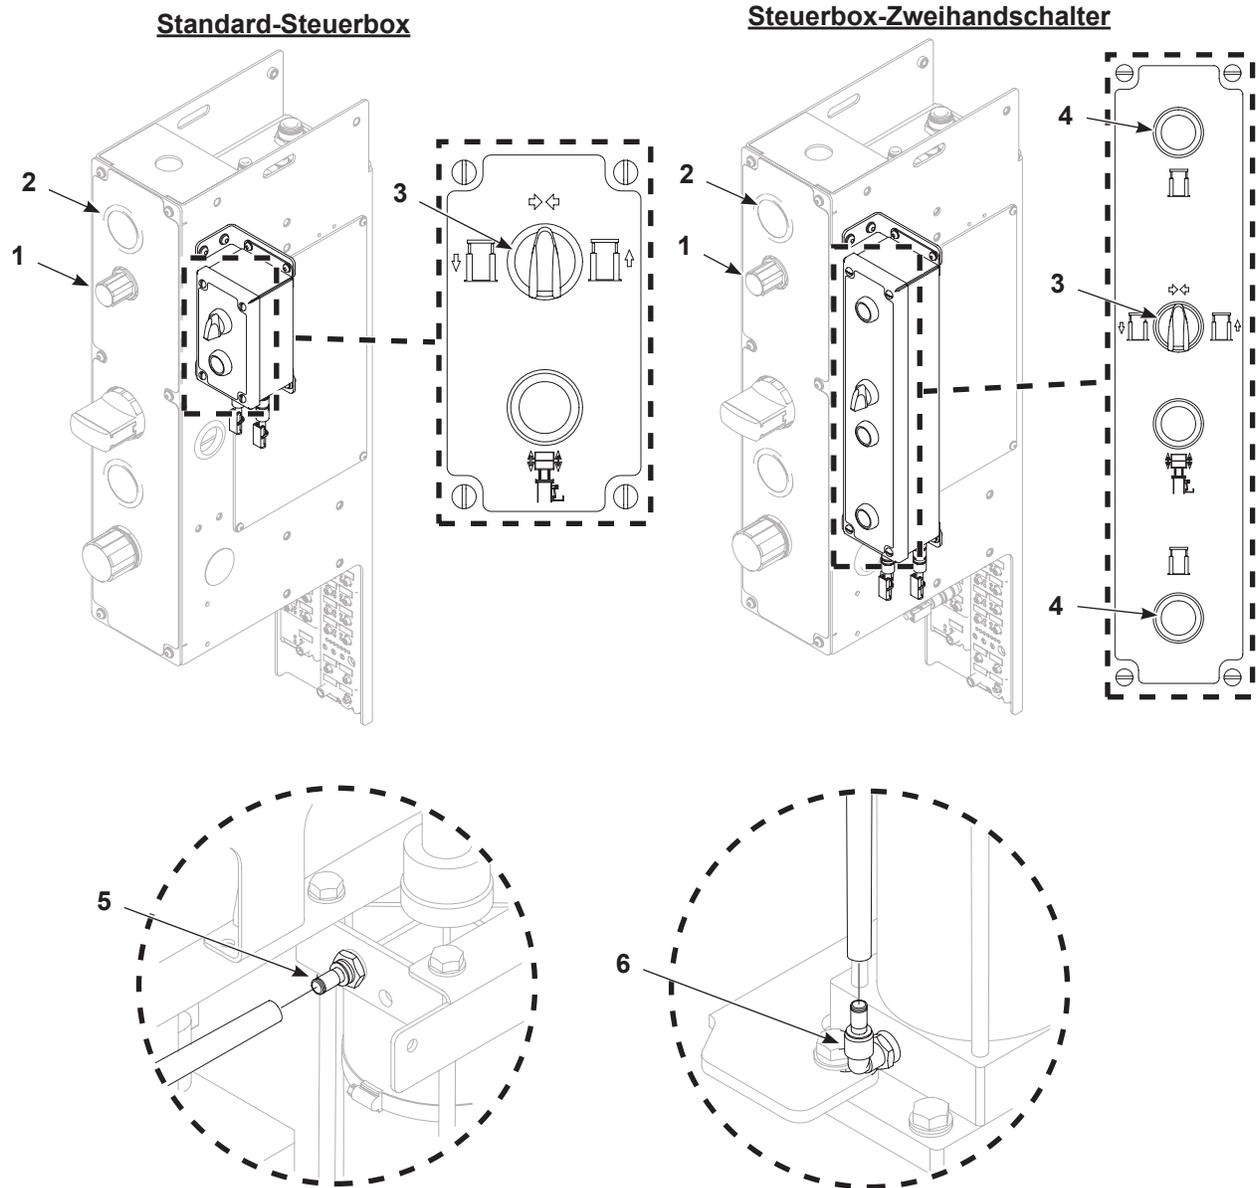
Druckentlastungsverfahren für Hubwerkzylinder
